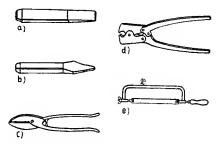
Trennwerkzeuge; Flachmeißel (a), Kreuzmeißel (b), Handblechschere (c), Hebelvorschneider (d) und Handbügelsäge (e)
